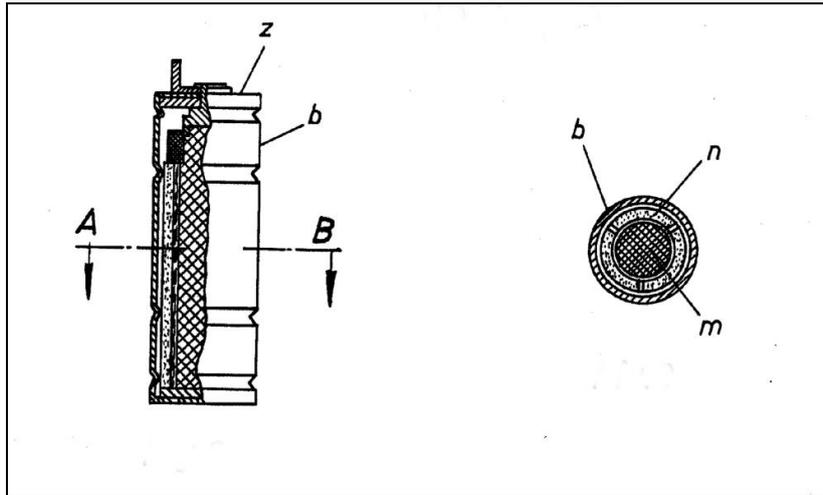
Detalle de uno de los elementos de la batería (Arch. J.M. Sanchis)
